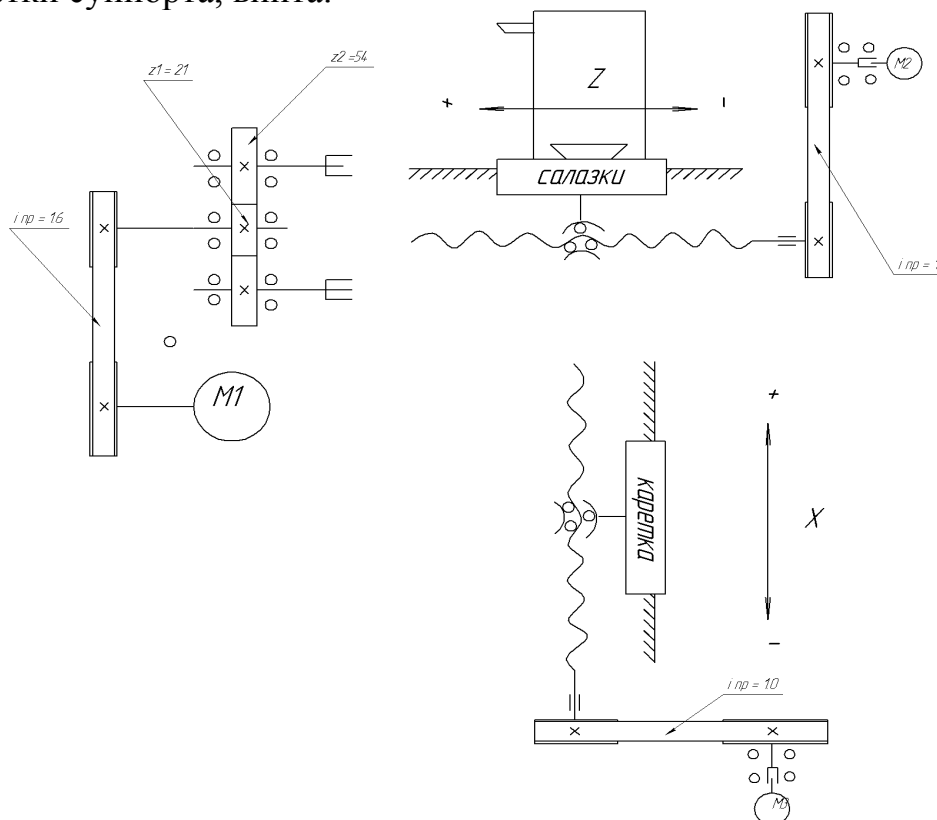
Кинематическая схема станка модели ПЗ-01
